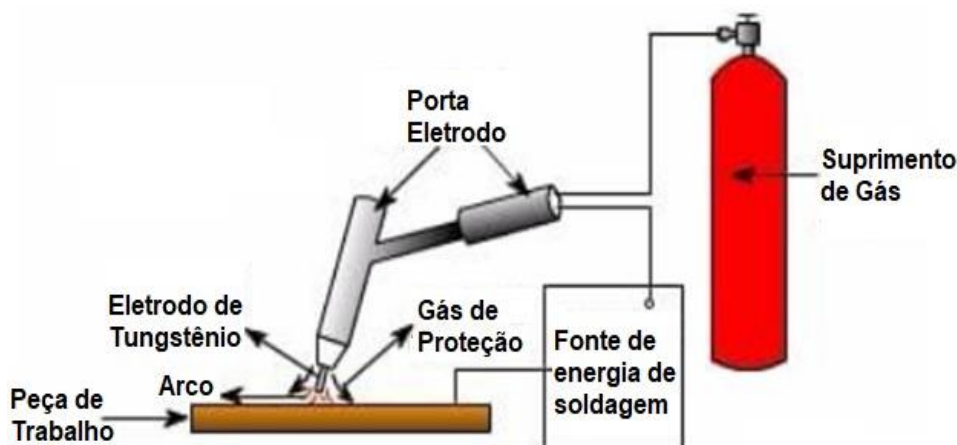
Princípio de funcionamento da soldagem TIG (Kumar e Bharathi, 2016),
